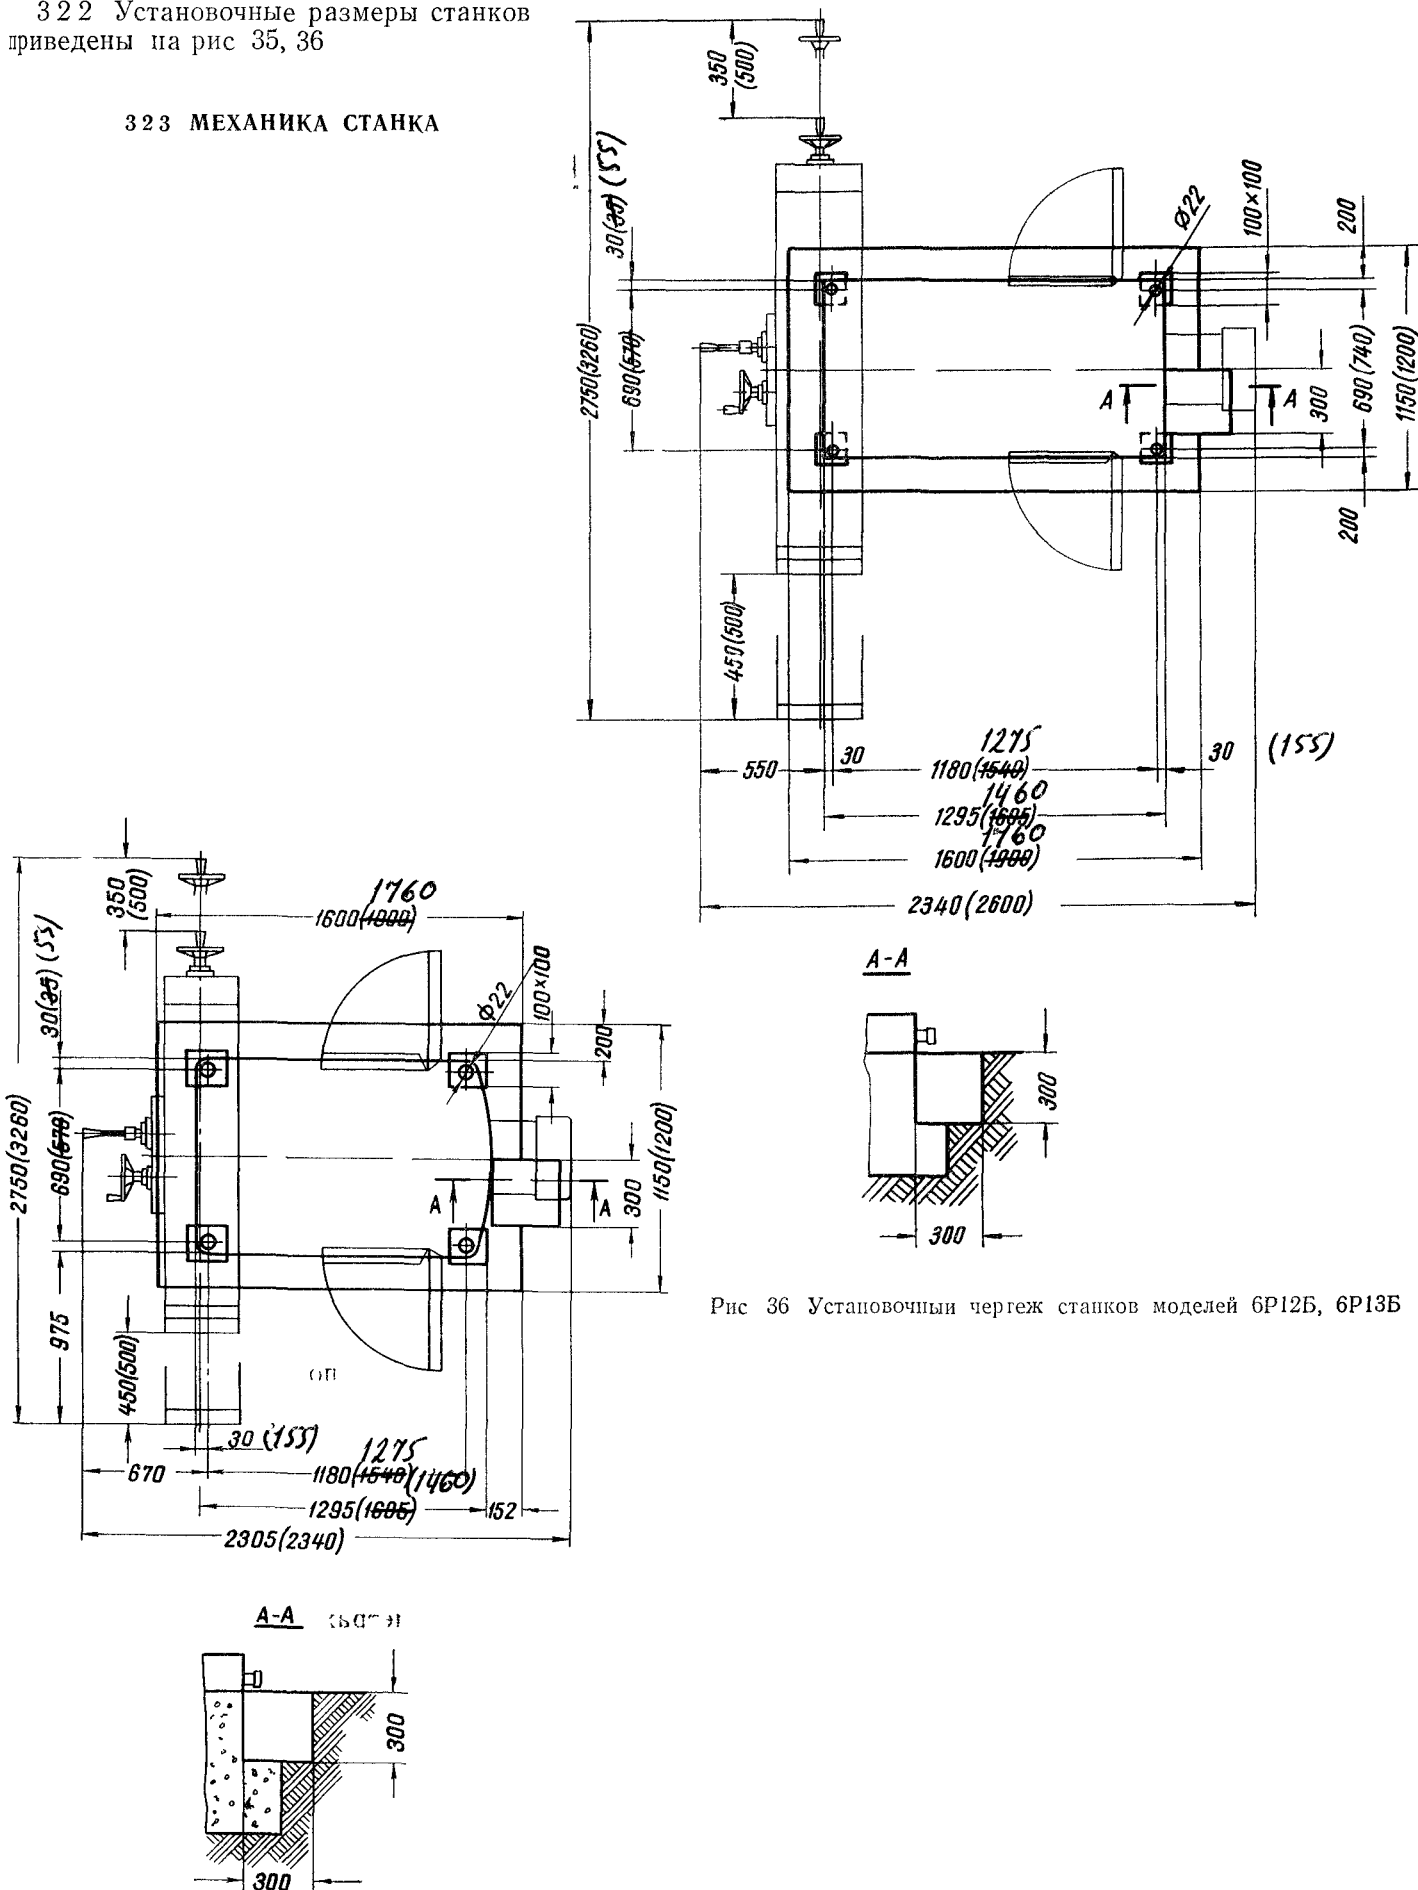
Установочный чертеж станков моделей 6P12Б, 6P13Б
